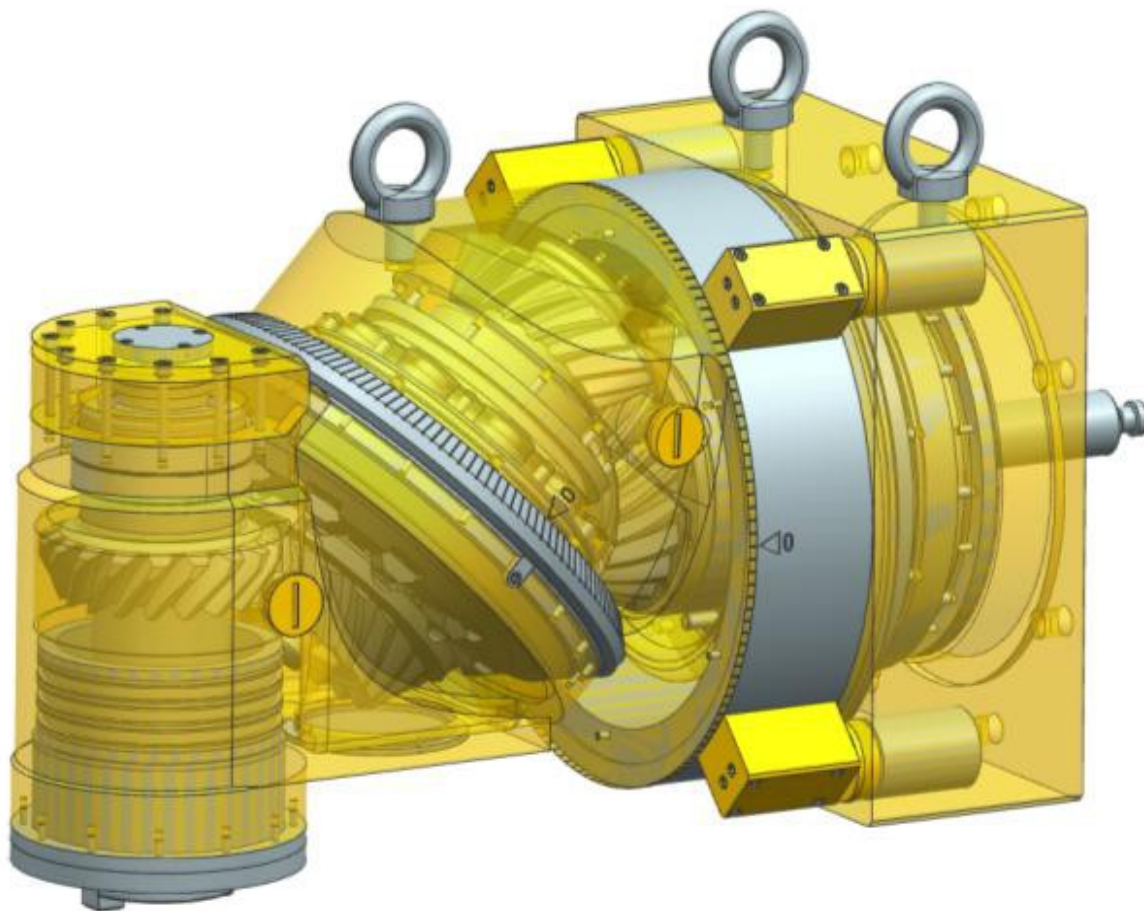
Frézovací příslušenství [ŠKODA MACHINE TOOL 11/ 2015]
